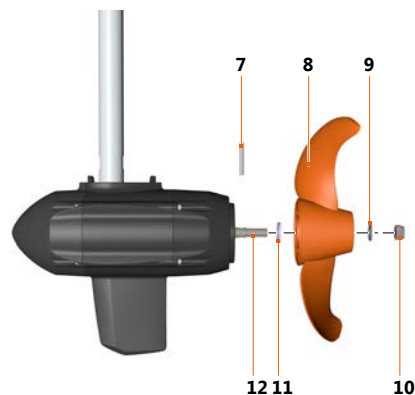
Fissaggio dell'elica Ultralight 1103 A/AC
